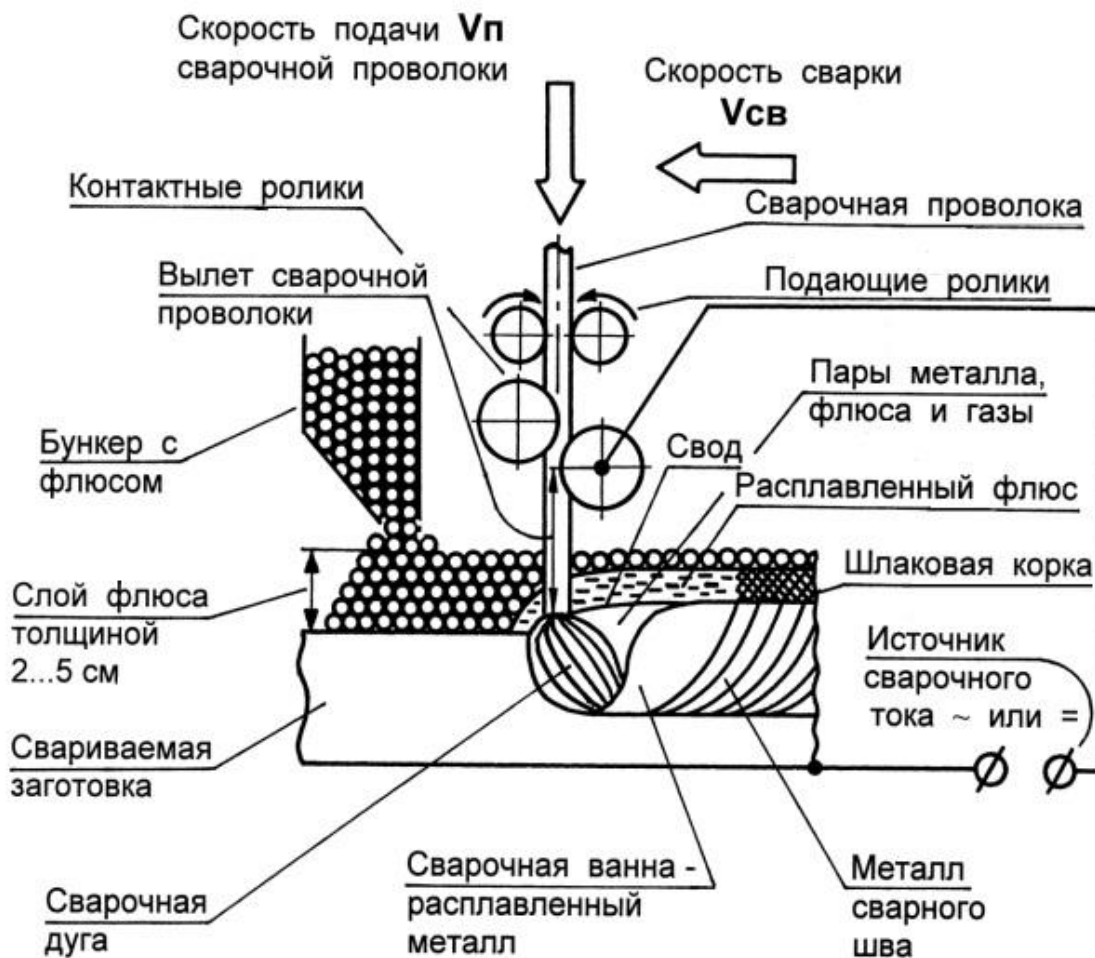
Схема процесса автоматической сварки под слоем флюса [20]
